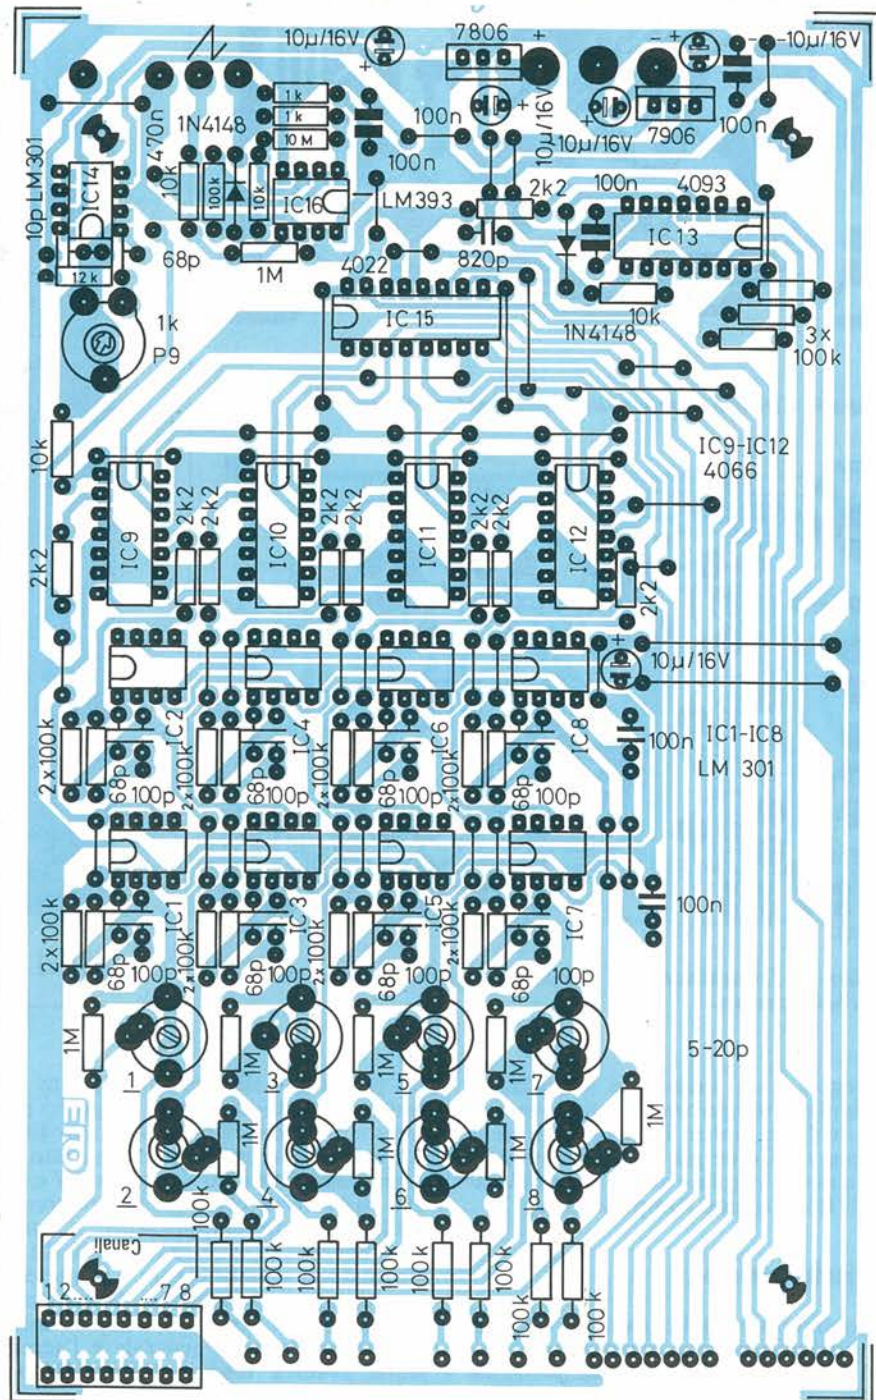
Disposizione dei componenti sul circuito stampato generale.
